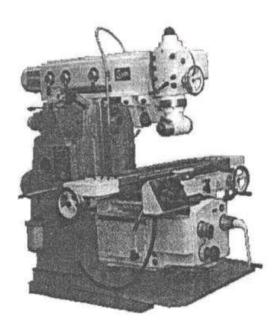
Станок фрезерный консольный широкоуниверсальный 6Т82Ш (6Т83Ш)
